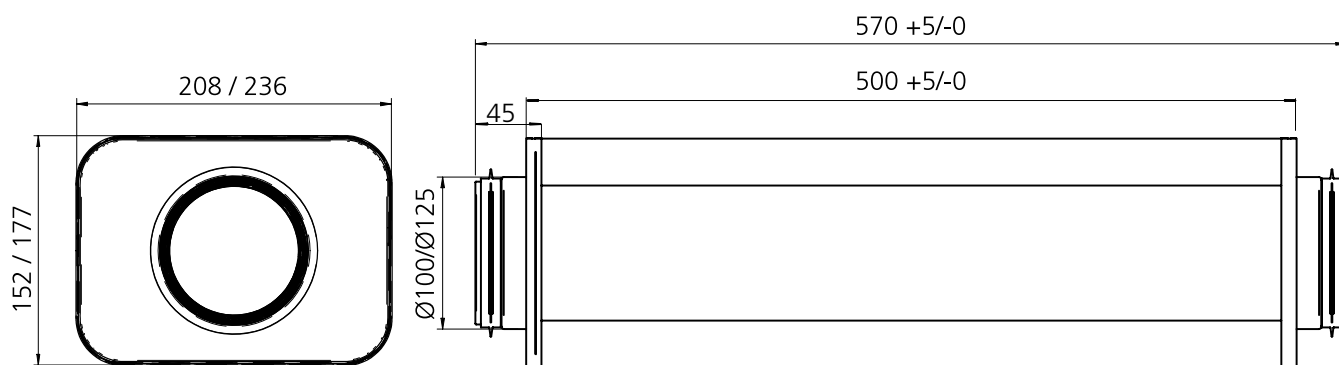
Maßzeichnung Schalldämpfer CLA Ø100-500 oder Ø125-500. Gehört zum Lieferumfang von allen PARAGON T-SAK und PARAGON T-EAK
